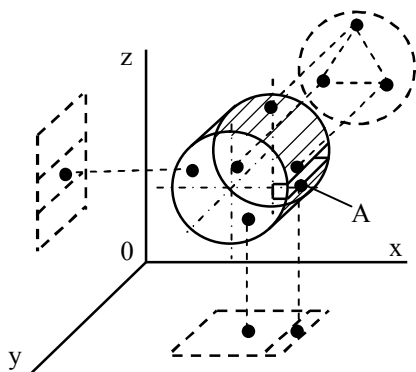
Базирование коротких цилиндрических заготовок
